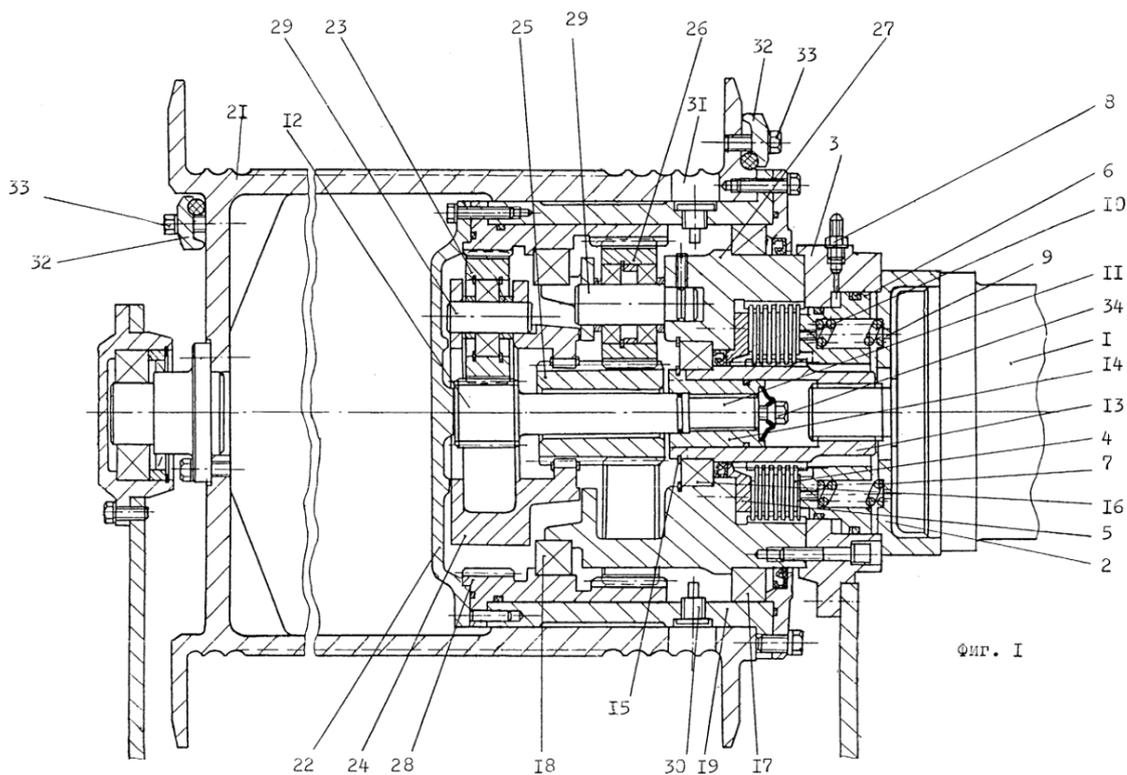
Чертеж лебедки с планетарным редуктором
